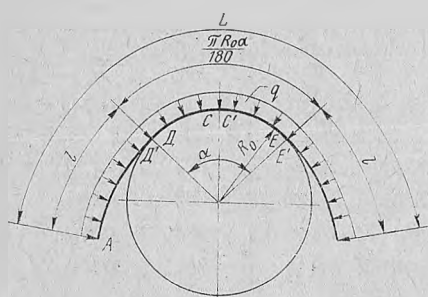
Изгиб полоски шпона по цилиндрической поверхности под действием равномерно распределенной нагрузки.
